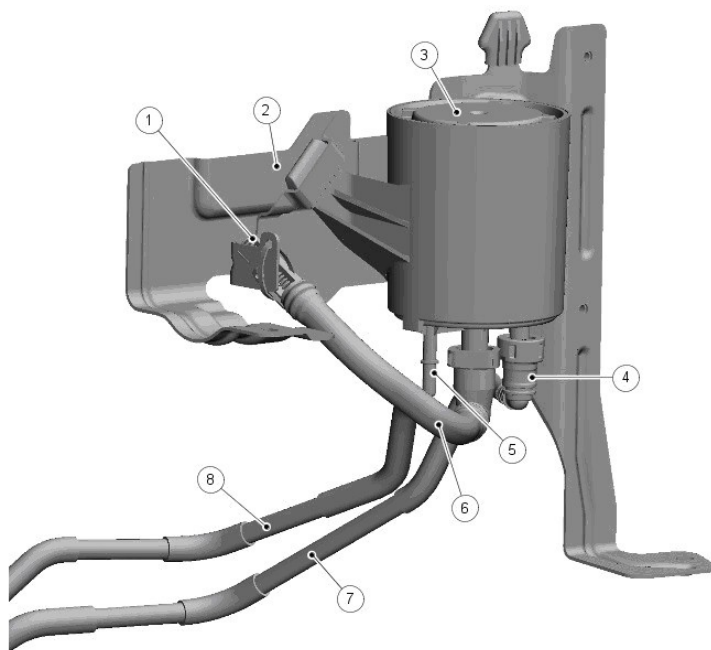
Угольный адсорбер бензинового двигателя 2.0L GTDi
